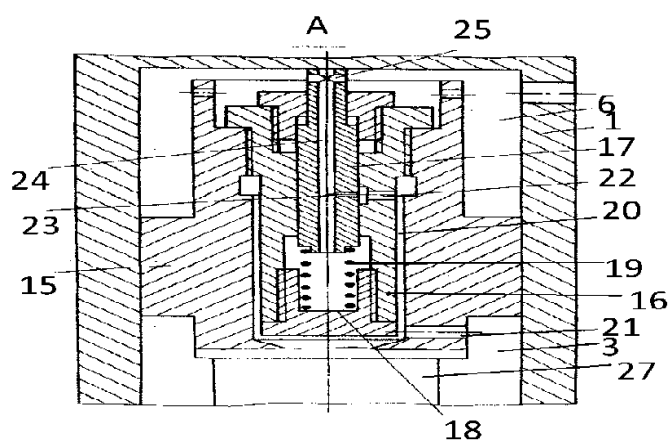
Устройство ведущего гидроцилиндра 1
